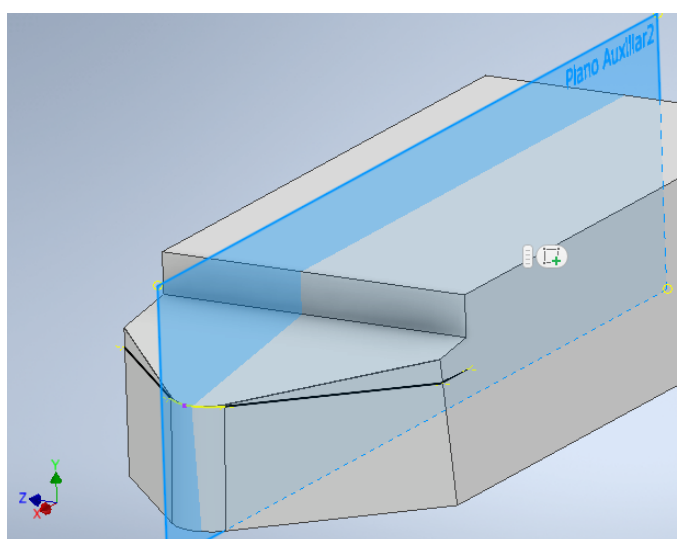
Criação do primeiro Plano Auxiliar 2, ou Plano Dorsal
